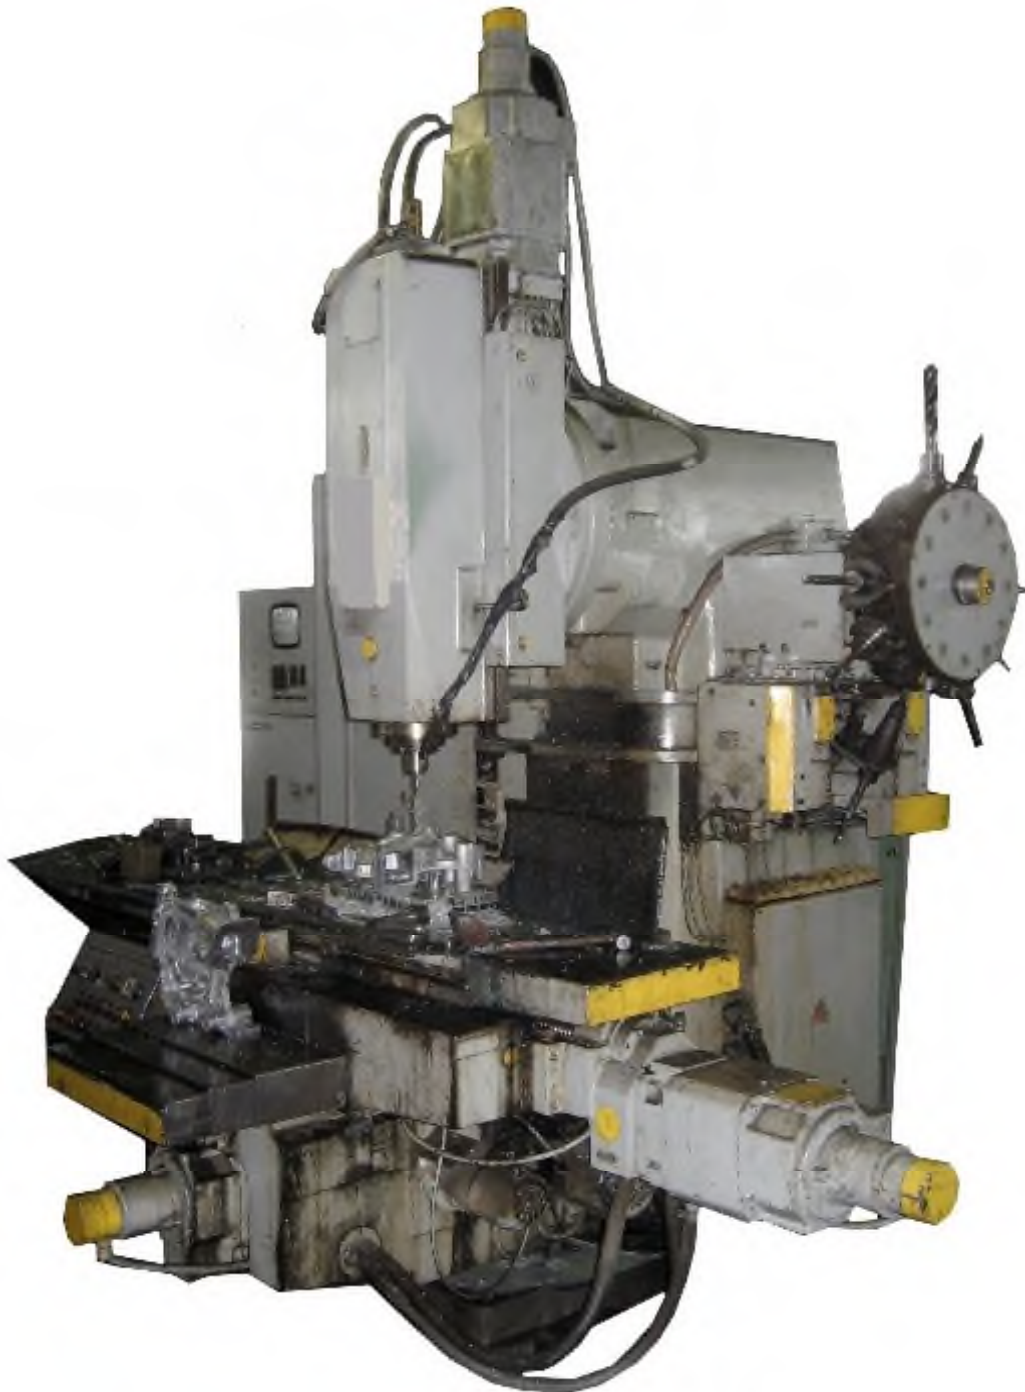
Вертикально-фрезерний верстат з ЧПК моделі 6Т13Ф3
